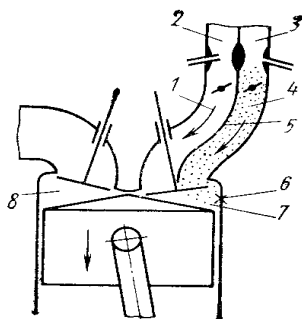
Конструктивная схема двигателя с бесфоркамерным факельным дожиганием:
